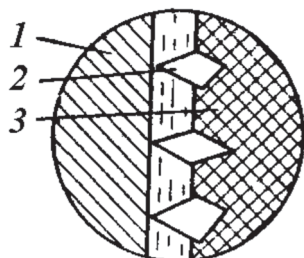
Схема анодно-механічного шліфування: 1 – заготовка; 2 – абразивні зерна; 3 – зв'язка шліфувального круга
